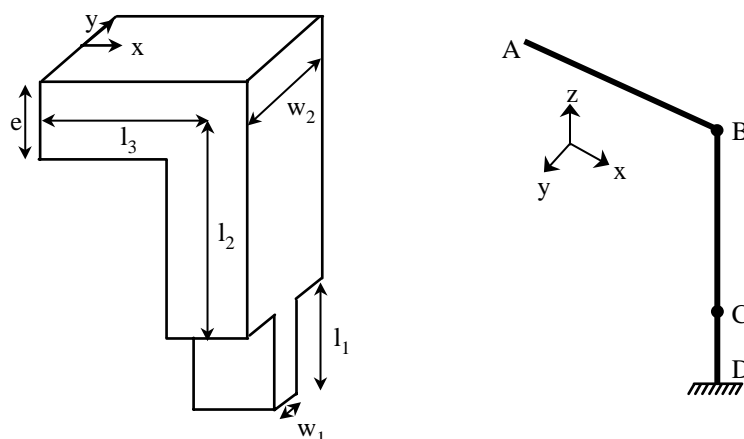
Modélisation de la broche par un empilement de poutres simples
